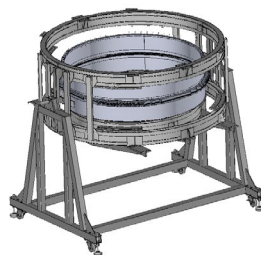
Оснастка для сборки модуля с корпусом внутри
